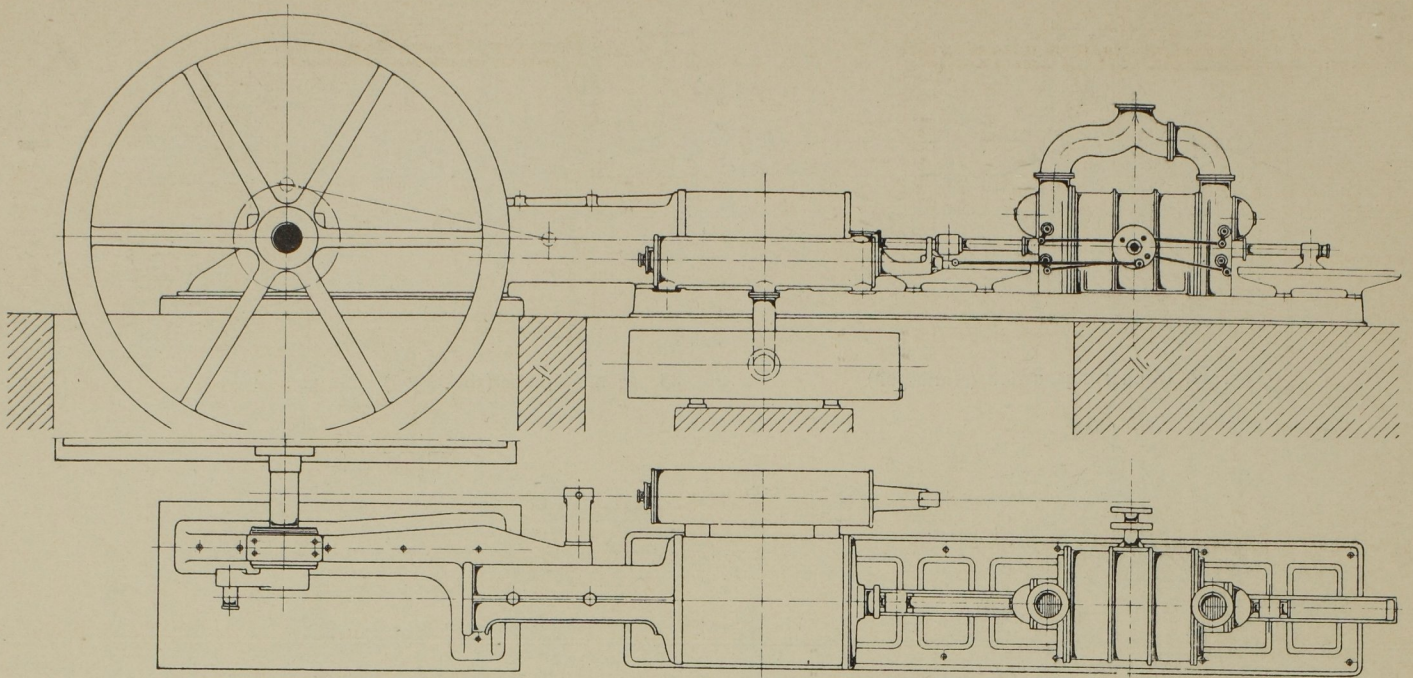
Seitenansicht und Grundriss. Masst. 1:100.
